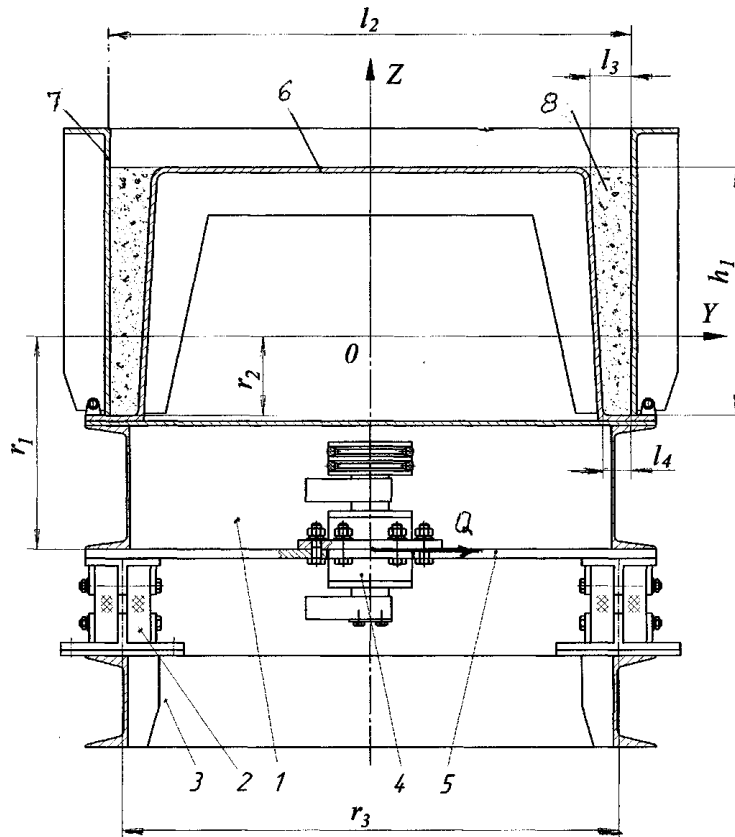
Розрахункова схема віброплощадки на стадії формування бічних стінок бетонного лотка у формі: 1 – рухома рама віброплощадки, 2 – пружна опора, 3 – опорна рама, 4 – віброзбудувач, 5 – опорна плита, 6 – осердя форми, 7 – поздовжній борт, 8 – бетонна суміш.
